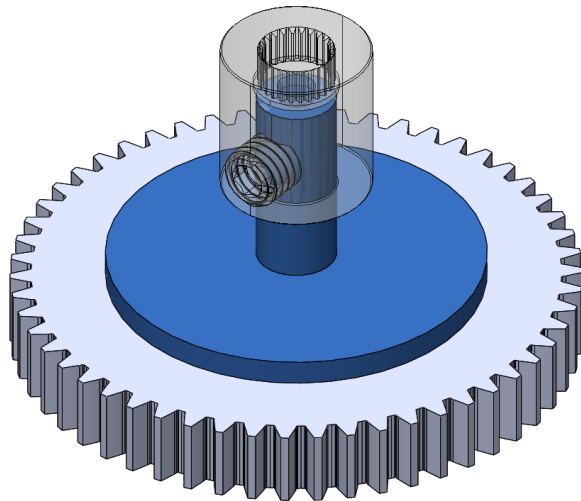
Eje para girar el engrane a partir del giro del servomotor.
